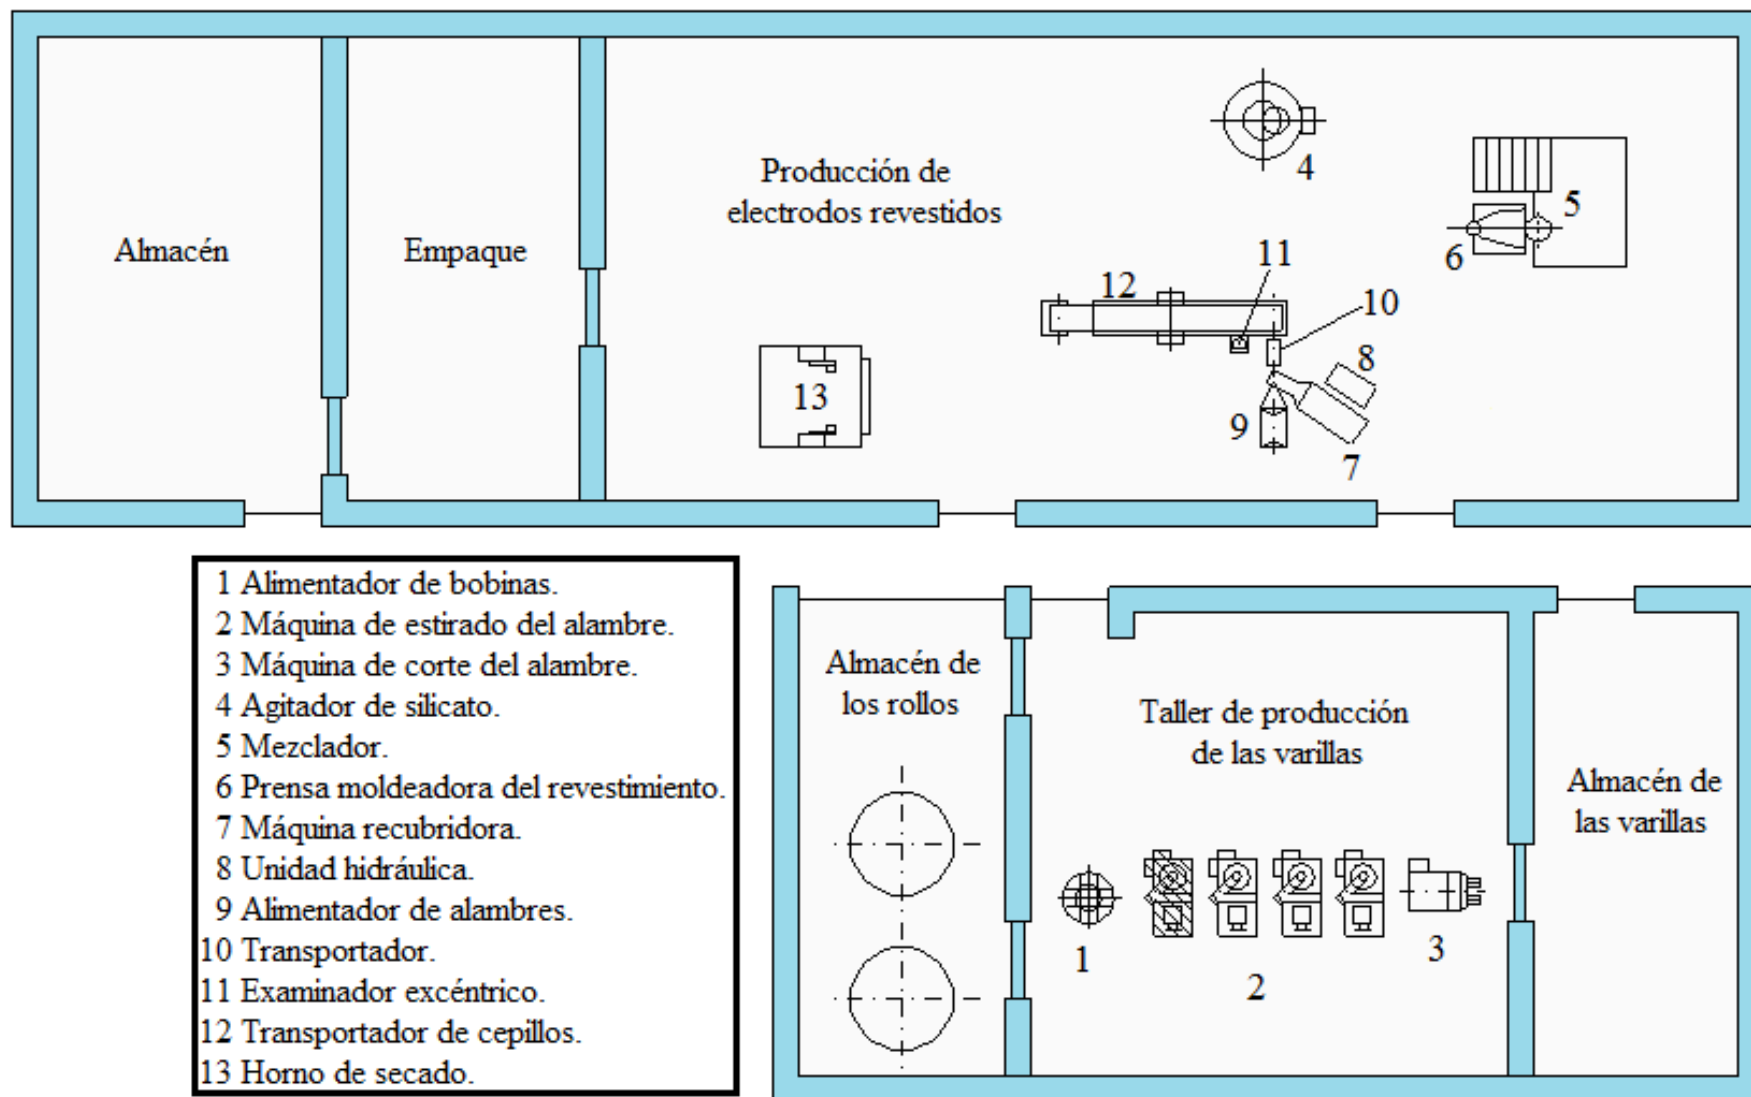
Vista en planta de la Planta de Producción de Electrodos Revestidos.
